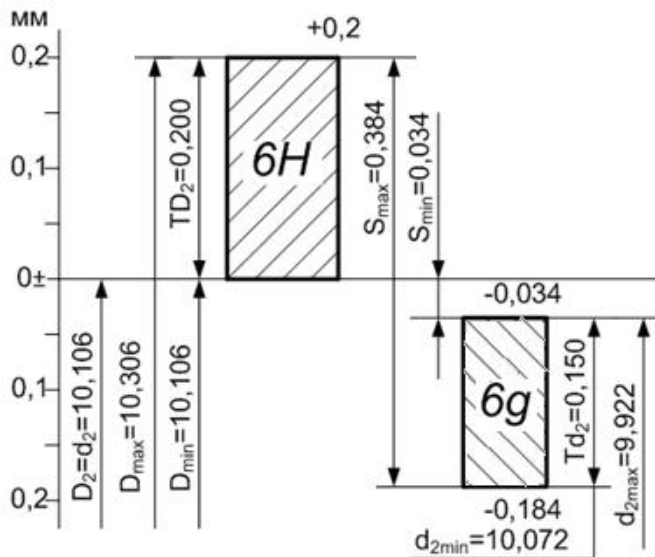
Схема розташування полів допусків нарізного з'єднання $M12-6H/6g$
